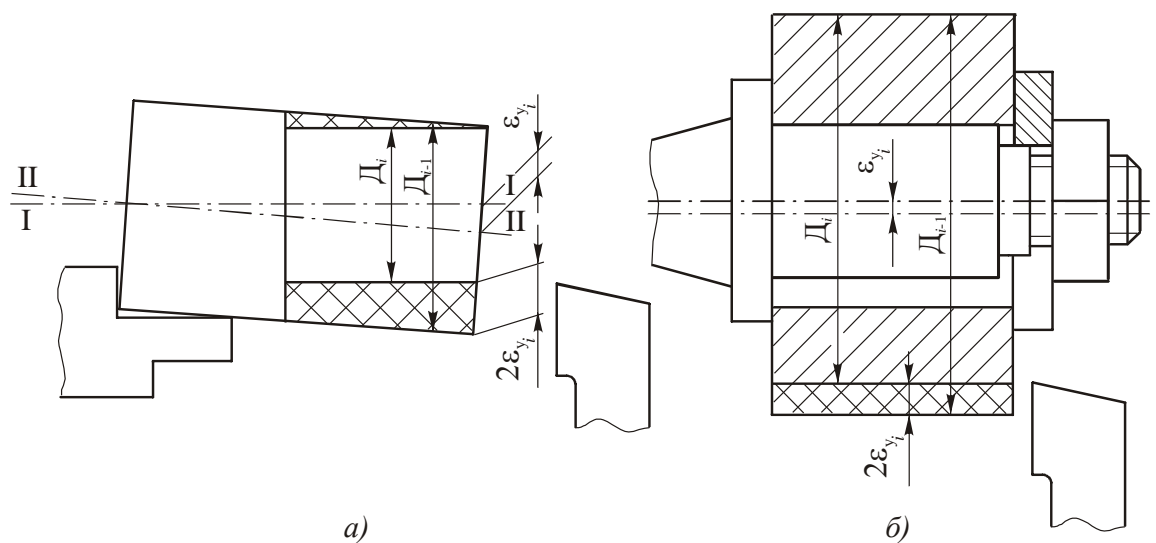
Схемы обработки заготовок, иллюстрирующие влияние погрешностей их установки на величину минимального припуска
